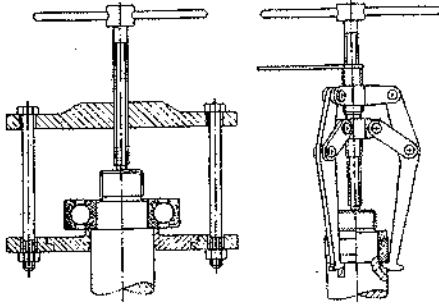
Rulmanların montaj ve demontajında çekiçle doğrudan vurulmaz
